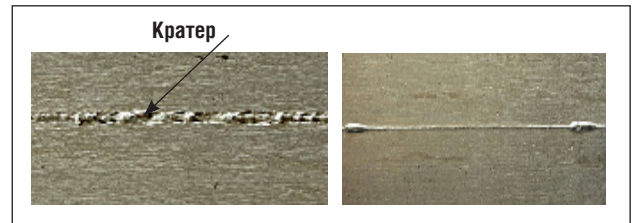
Шов на образце № 6, полученный сваркой излучением CO₂-лазера со скоростью 420 м/ч, ×3
